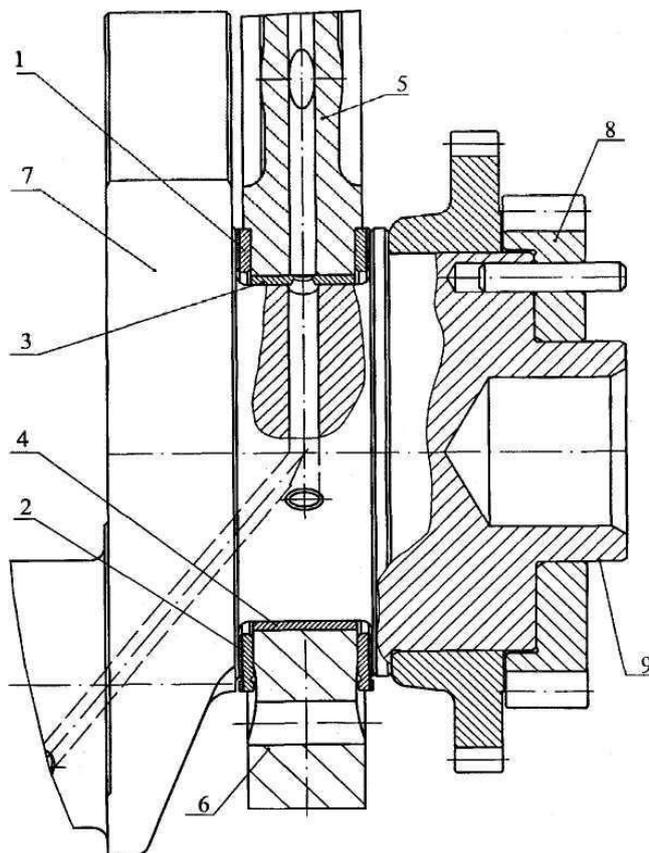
Установка упорных полуколец и вкладышей коленчатого вала: 1 - полукольцо упорного подшипника верхнее; 2 - полукольцо упорного подшипника нижнее; 3 - вкладыш подшипника коленчатого вала верхний; 4 - вкладыш подшипника коленчатого вала нижний; 5 - блок цилиндров; 6 - крышка подшипника коленчатого вала задняя; 7 - коленчатый вал; 8 - шестерня привода газораспределительного механизма; 9 - центрирующая шейка коленчатого вала.
